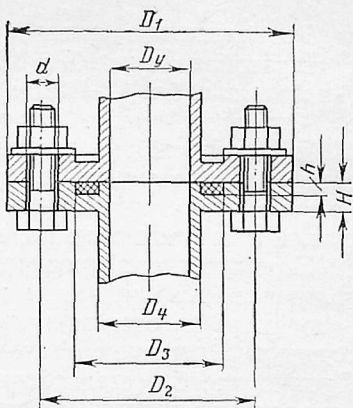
Типовая конструкция соединения с резиновым уплотнителем.
